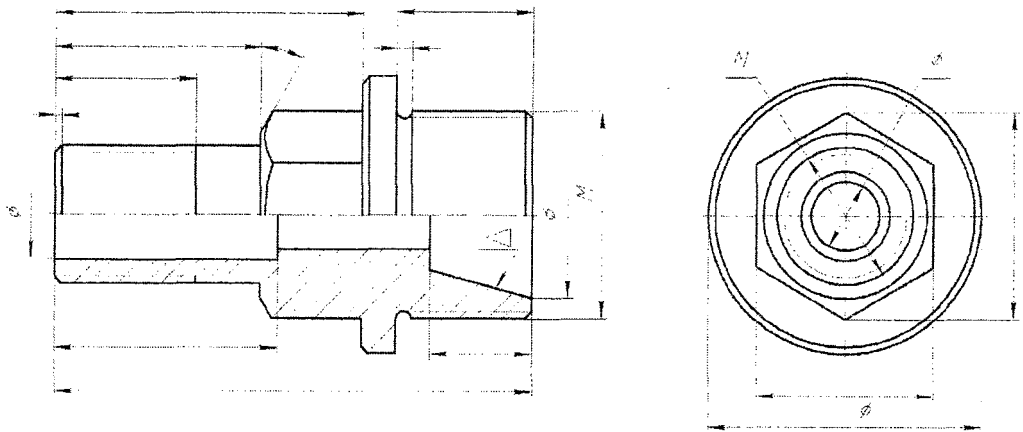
Пример простановки размеров на чертеже детали – штуцер
